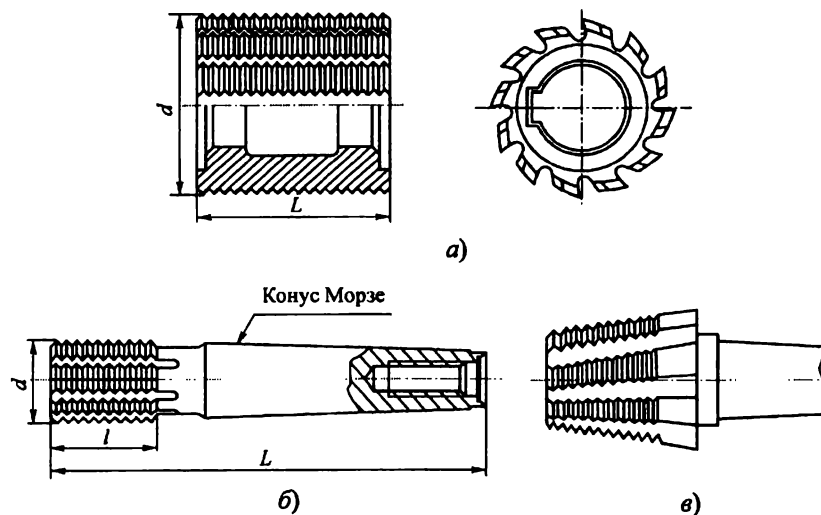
Гребенчатые резьбонарезные фрезы: *а* – цилиндрическая насадная; *б* – цилиндрическая концевая; *в* – для нарезания конических резьб
